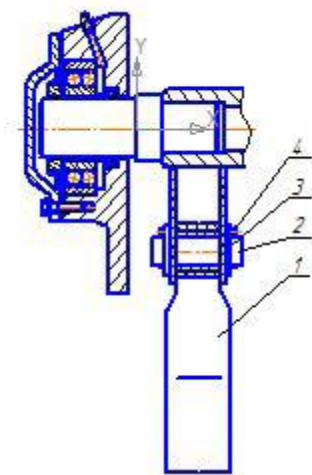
Ніж в зборі: 1 – ніж; 2 – палець; 3 – шайба; 4 - шплінт
